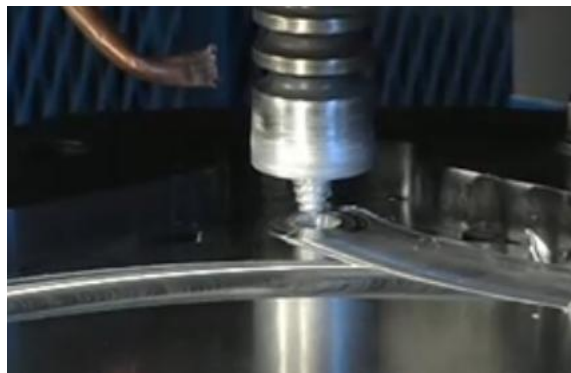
Fin del recorrido de soldado y salida de la herramienta
